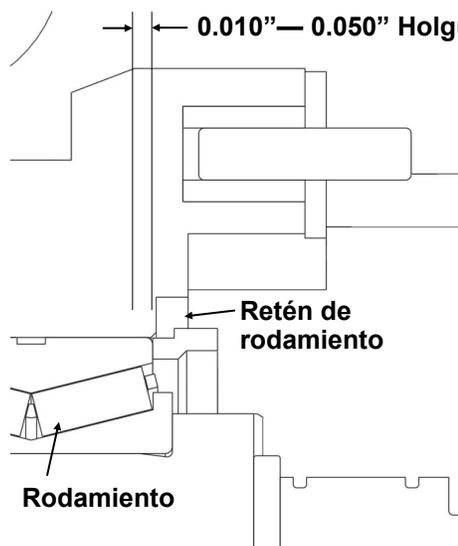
Tolerancia de retenes de los rodamientos
